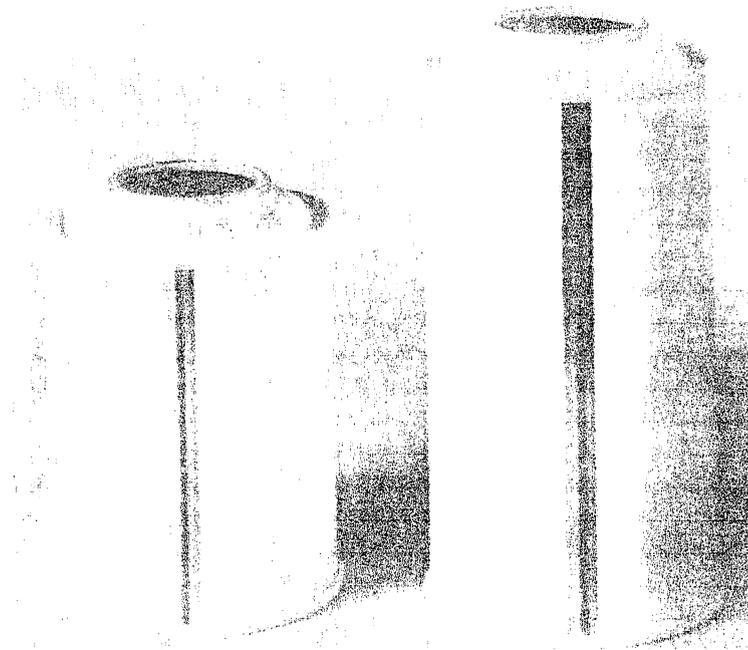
Envase fabricado soldadora Soudronic
